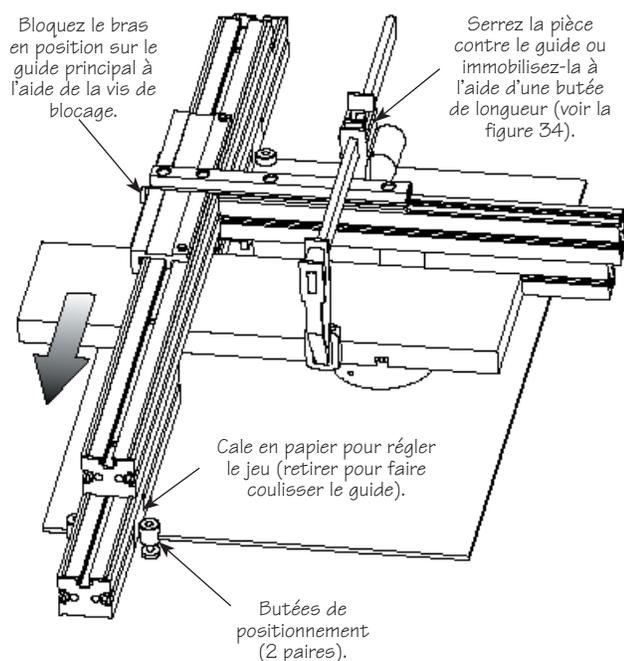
Usinage perpendiculaire de pièces de largeur supérieure à 4 po (100mm).
